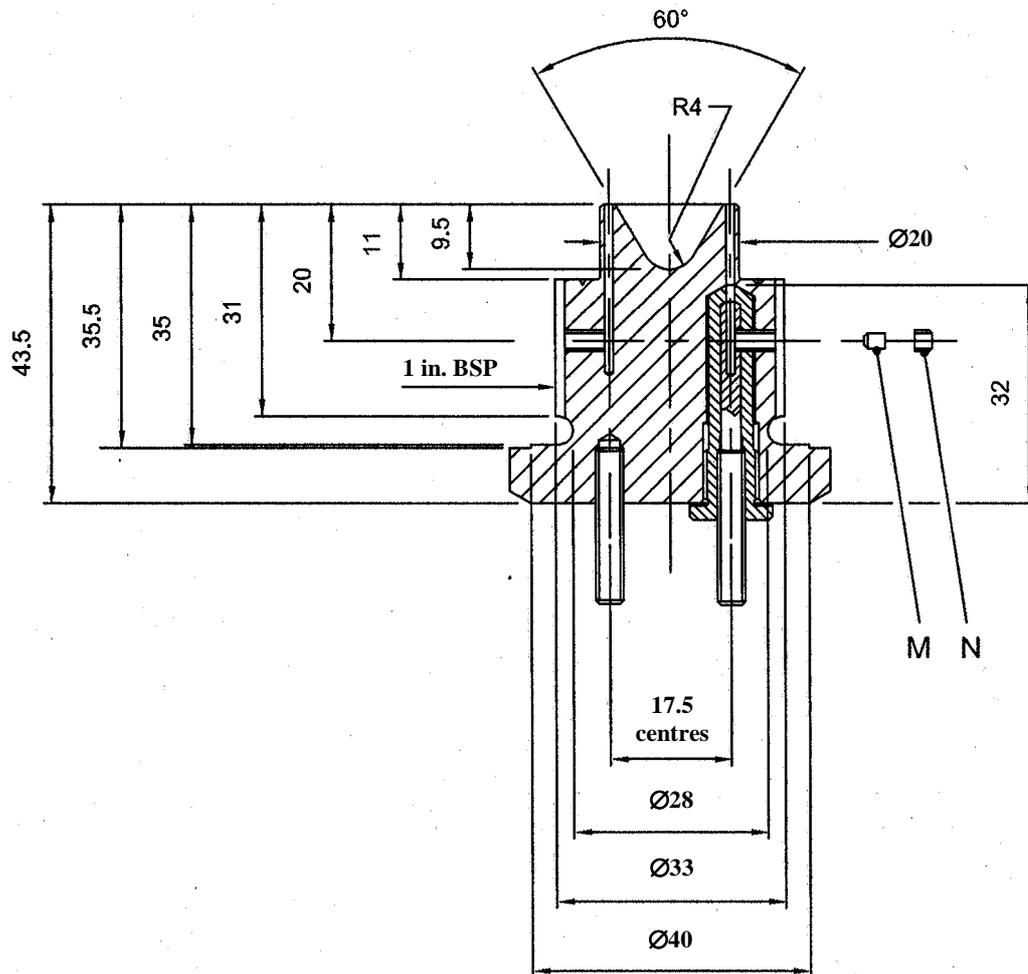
BOUCHON À ÉVIDEMENT CONIQUE ASSEMBLÉ
